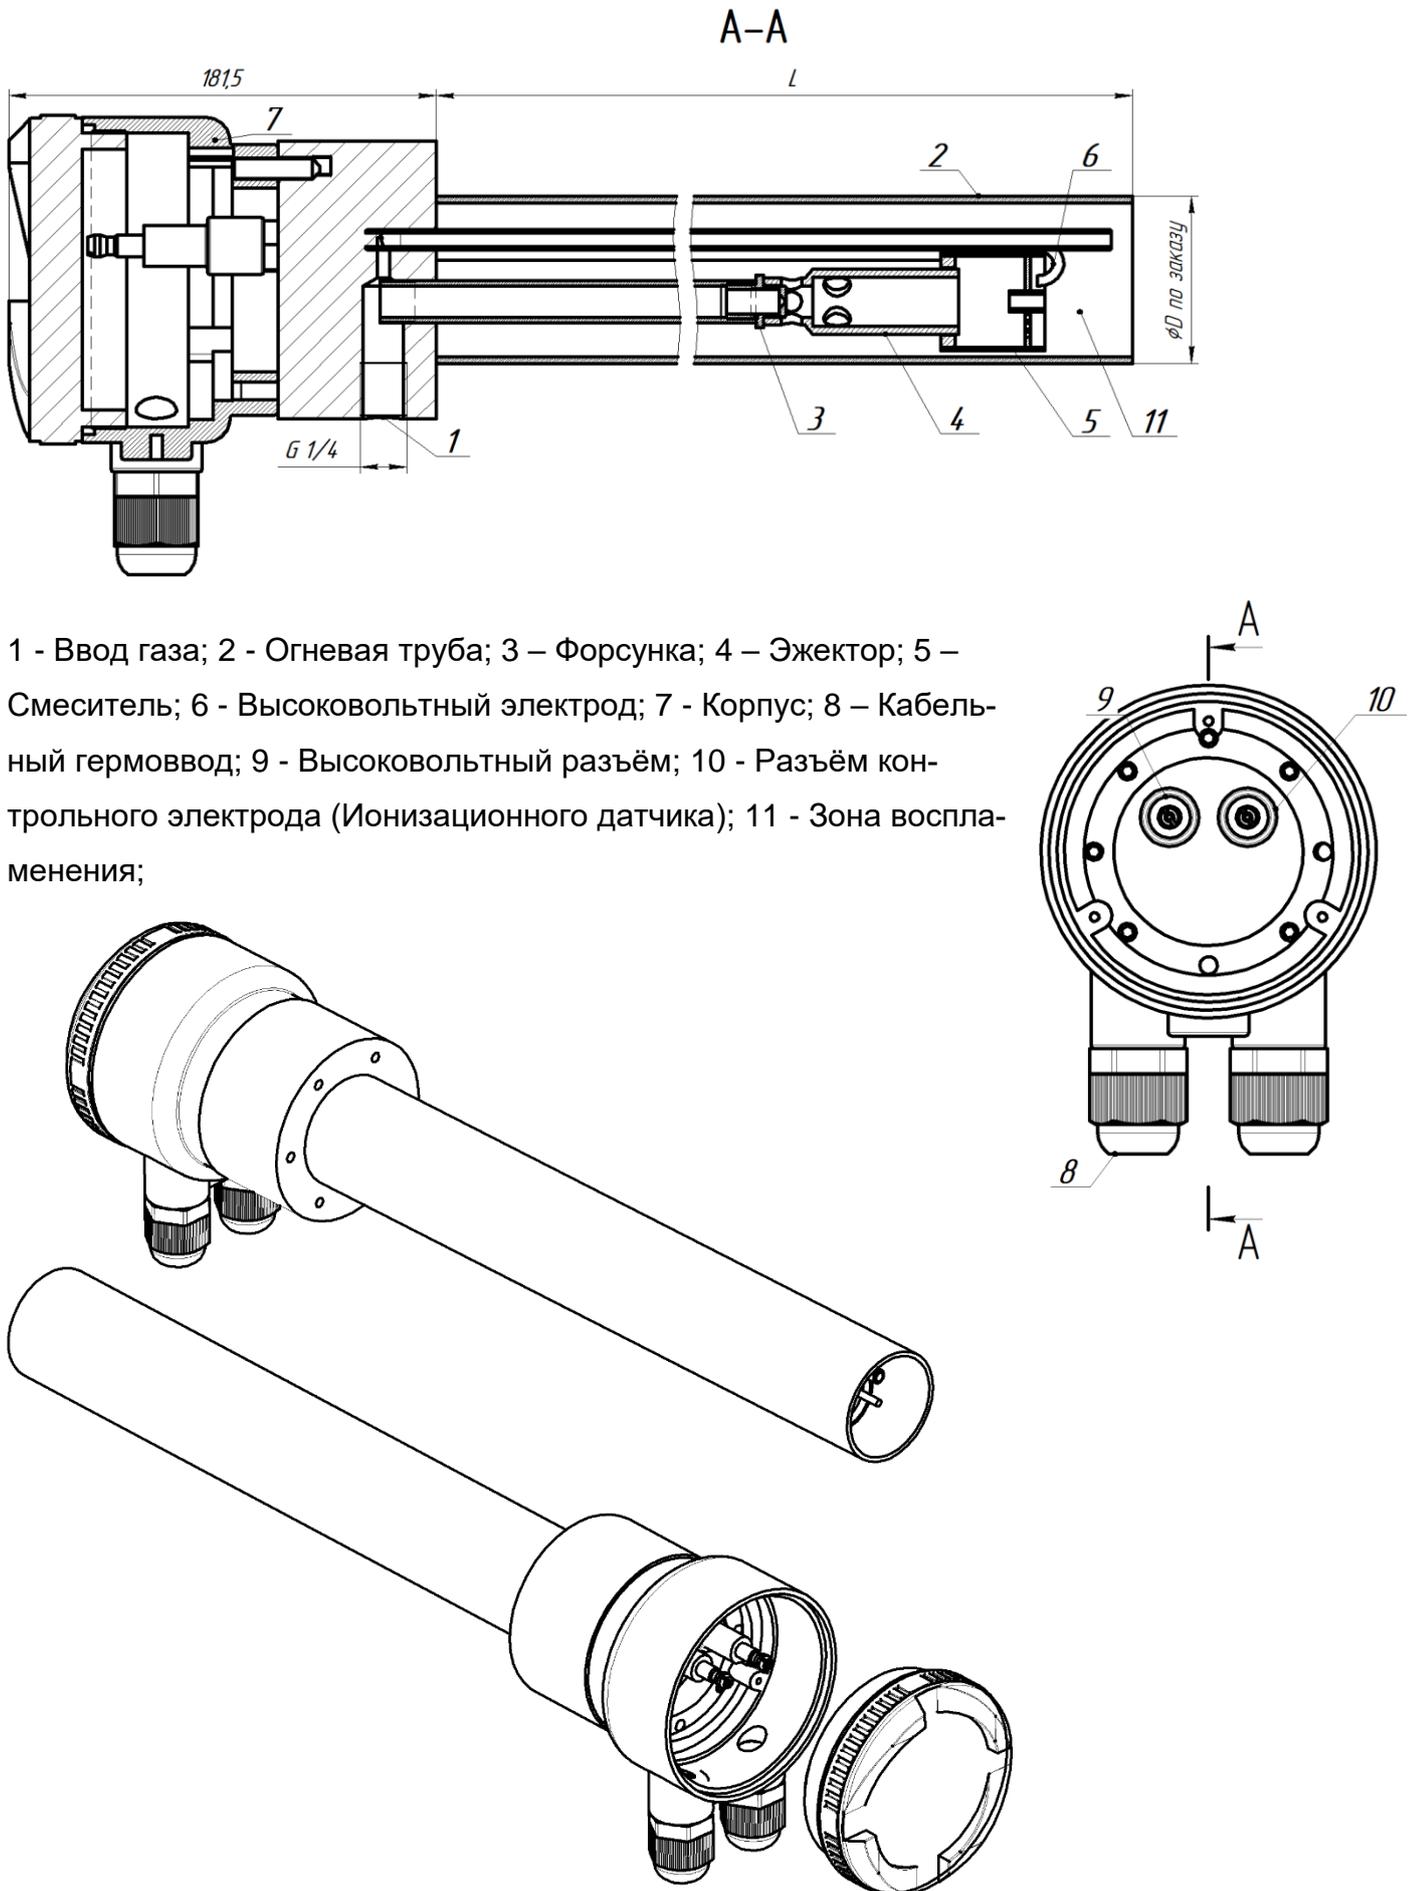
Устройство и габаритные размеры ЗИГ-45(60)-IP65 без подвода воздуха
